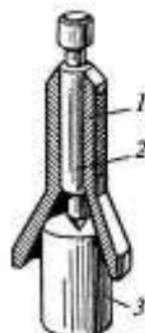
Приспособление для накернивания центровых отверстий без предварительной разметки:
